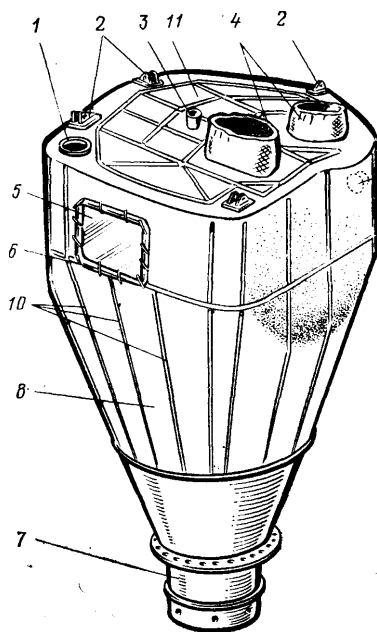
Бак для химикатов из стеклоткани: 1 — фланец крепления заправочного приспособления; 2 — узлы крепления бака; 3 — фланец с раструбом под чехол соединительного вала мешалки; 4 — чехлы загрузочных рукавов; 5 — крышка ремонтного люка; 6 — болты крепления крышки люка; 7 — выпускная горловина; 8 — корпус бака; 9 — окуляр; 10 — стрингеры жесткости; 11 — верхняя крышка
